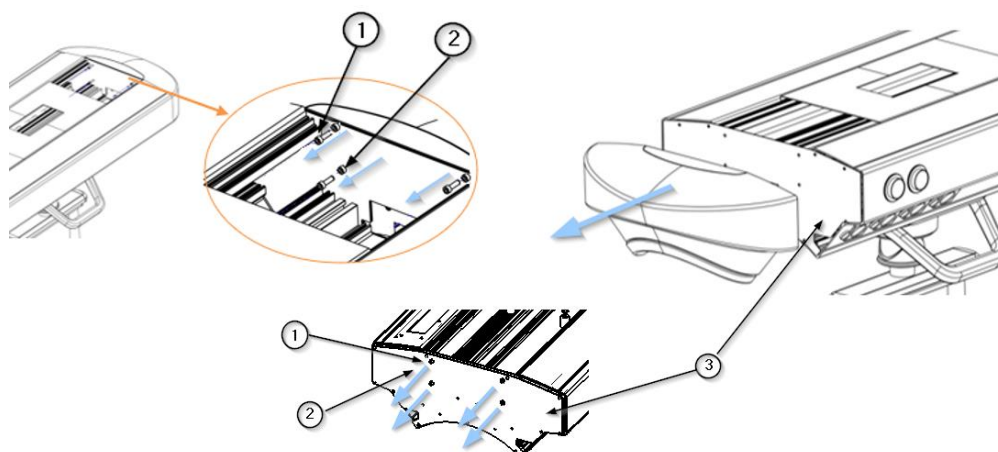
Desmontaje / montaje de testeros en cuerpo principal ABITUS
